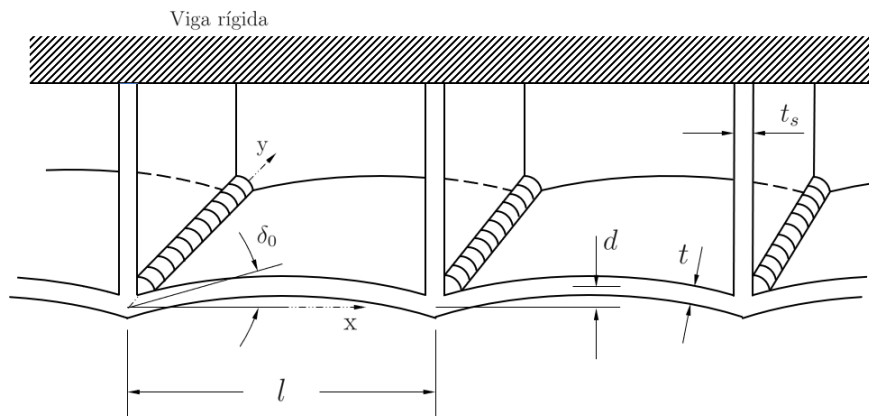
Soldadura de filete en un marco restringido. [13]
